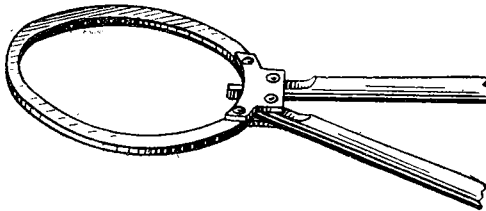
Приспособление для снятия и установки поршневых колец на поршень двигателя
